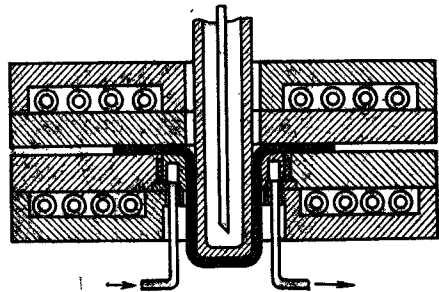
Схема вытяжки с местным подогревом заготовки и охлаждением дна детали
